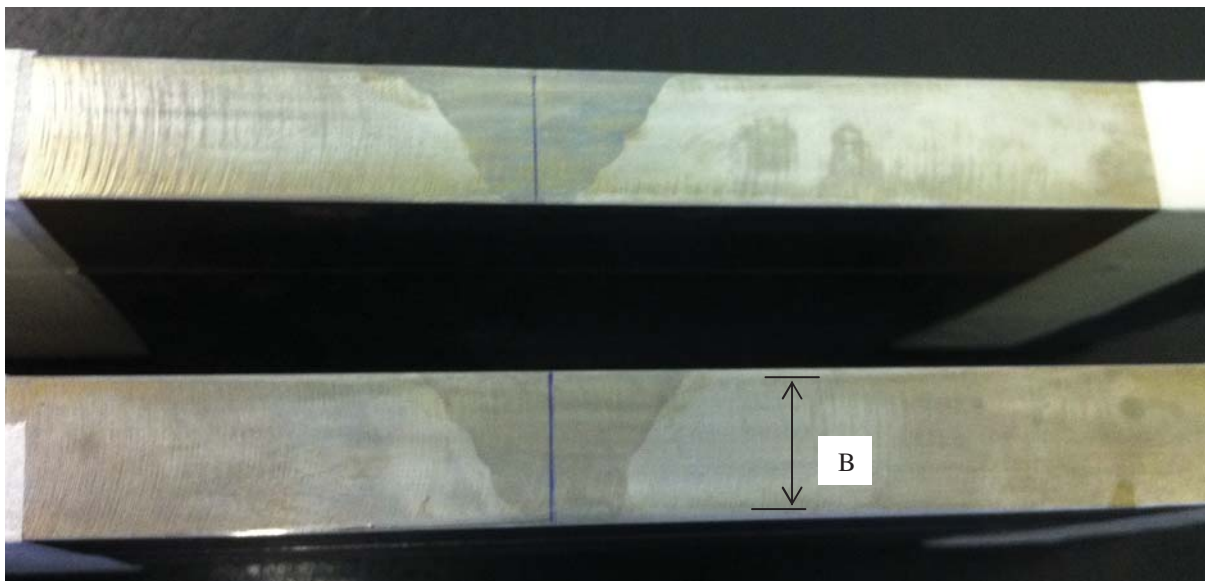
Corpos de prova SE (B) (solda) após o ataque químico – Seção transversal (B = 14 mm)
